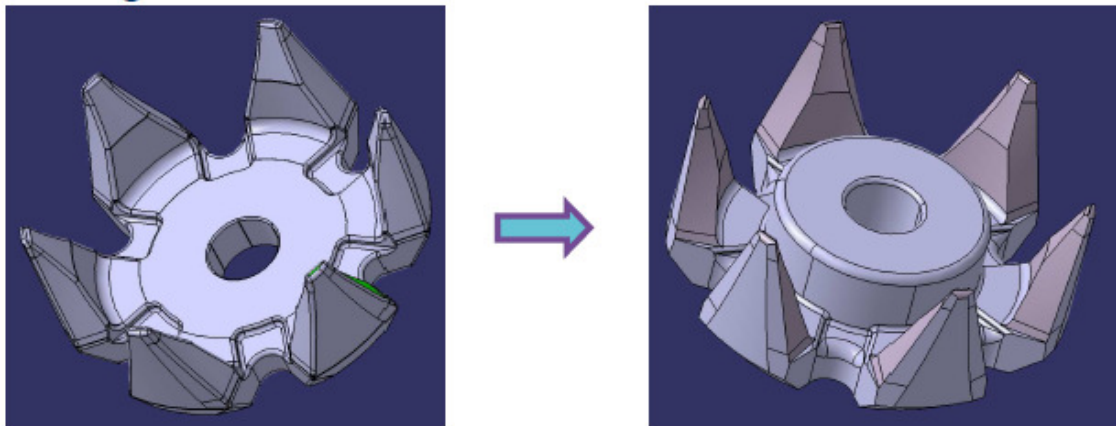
Conjunto de garras do rotor com cilindro acoplado
